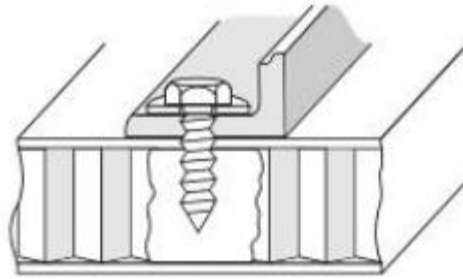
Mechanický insert s ochranným kroužkem na obou stranách [12]
